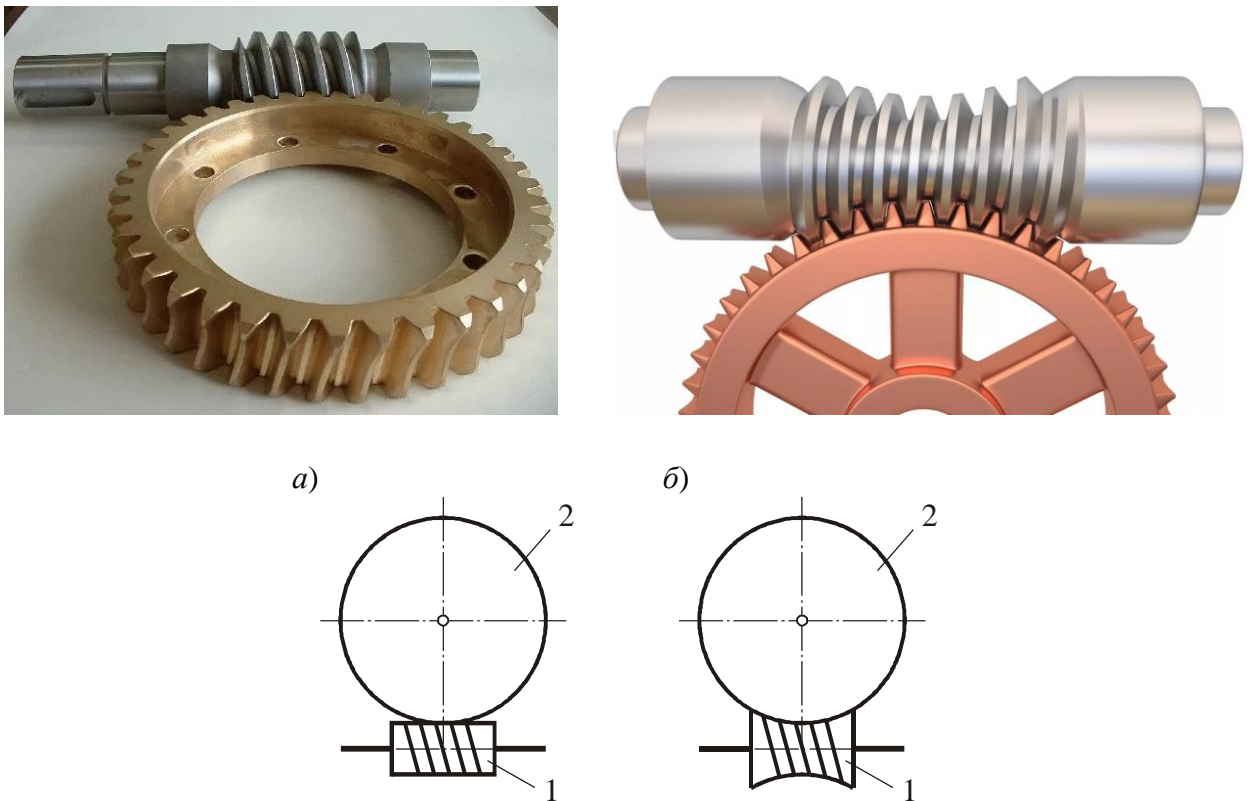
Схемы червячных передач: *а* – цилиндрической; *б* – глобоидной
